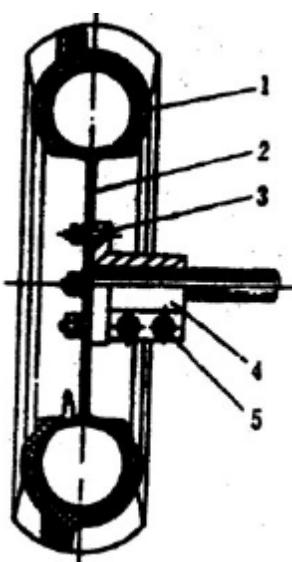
Схематическое изображение регулировки профиля качения колеса
